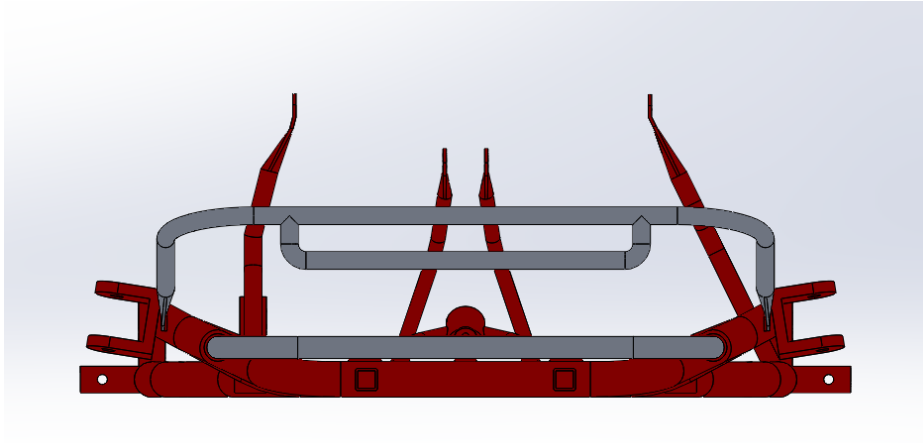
vista frontal del conjunto de paragolpes frontal. Fuente: propia.
